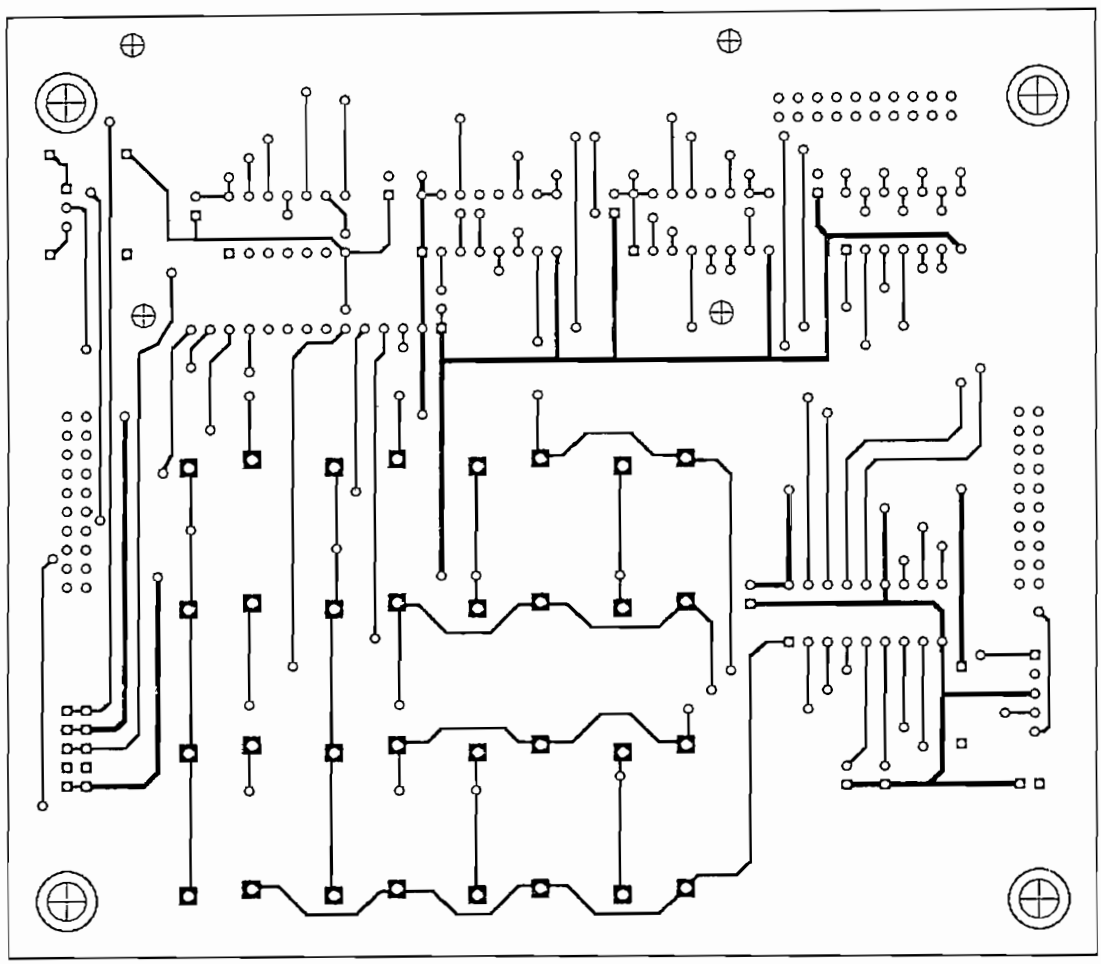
Tarjeta impresa Tedisco , bottom - soldadura
